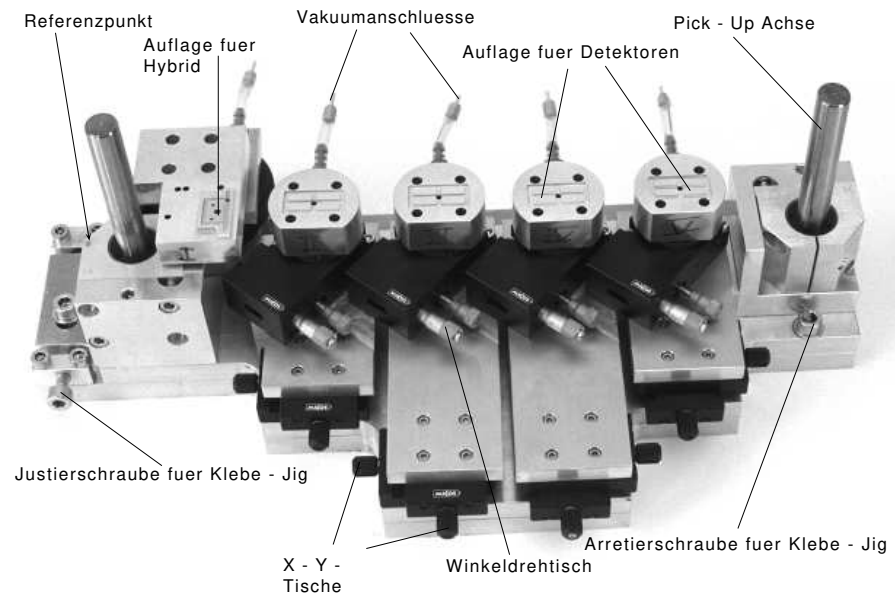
Der Klebejig, Sicht von schräg oben. Für die Ausrichtung jedes einzelnen Detektors stehen x - y -Tische und ein Winkeldrehtisch zur Verfügung. Der gesamte Jig wird mit einer Justierschraube auf der Koordinatenmeßmaschine ausgerichtet.
